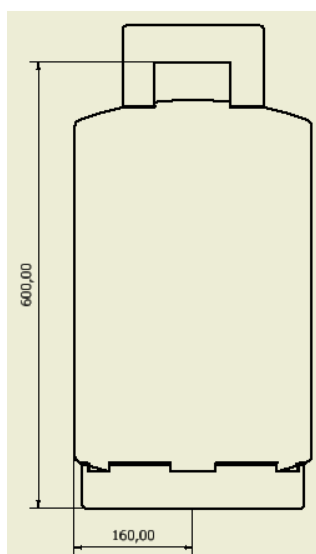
Dimensiones de un tanque de gas de 15kg.
